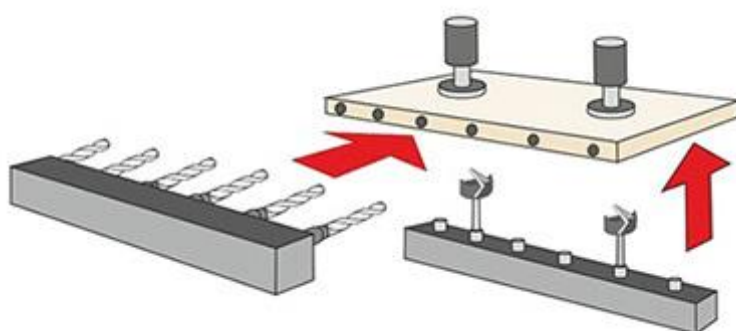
Однотраверсный сверлильно-присадочный станок
